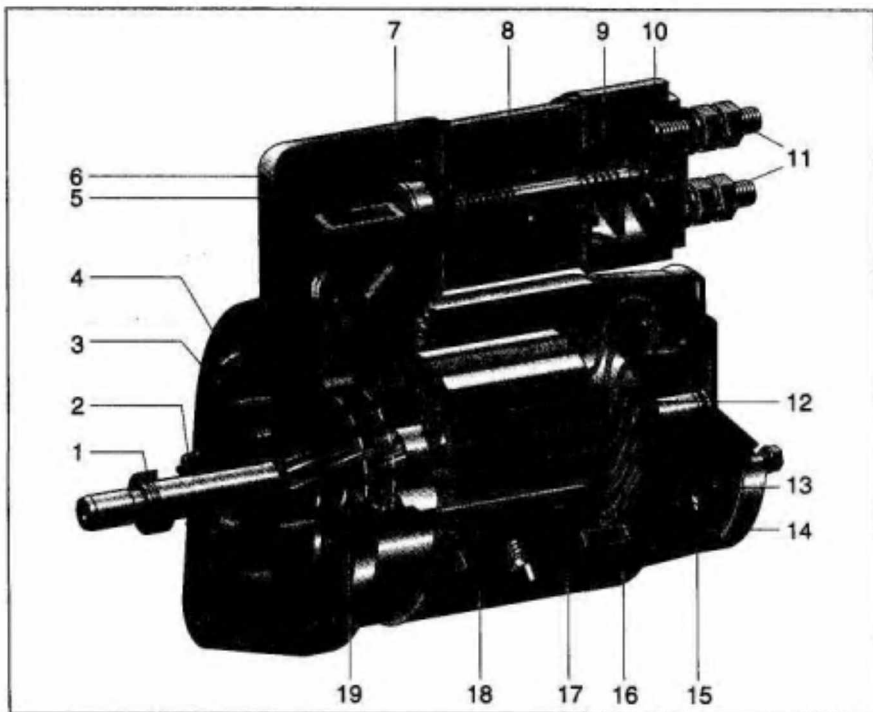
Стартер 39.3708:1 — ограничительное кольцо; 2 — шестерня привода; 3 — ролик муфты свободного хода; 4 — муфта свободного хода; 5 — рычаг привода; 6 — крышка стартера со стороны привода; 7 — якорь реле; 8 — катушка реле; 9 — контактная пластина; 10 — крышка реле; 11 — контактные болты; 12 — коллектор; 13 — щетка; 14 — кожух; 15 — крышка со стороны коллектора; 16 — корпус стартера; 17 — полюс статора; 18 — якорь стартера; 19 — поводковое кольцо
